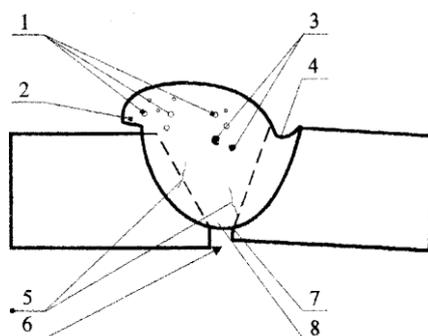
Дефекты сварного соединения: 1 – поры; 2 – наплыв; 3 - раковины; 4 – подрез; 5 – трещины; 6 – неправильная сборка стыка; 7 - несплавление; 8 – непровар корня шва
